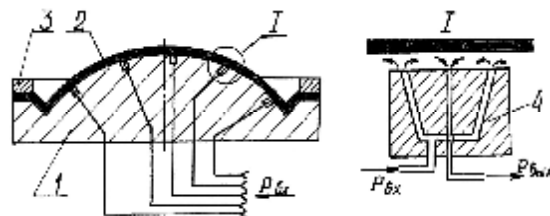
Вариант расположения струйных датчиков для определения прилегания заготовки к матрице: 1 – матрица; 2 – заготовка; 3 – прижимное кольцо; 4 – корпус датчика; $P_{\text{вх}}$ – питающее давление; $P_{\text{изх}}$ – измеряемый параметр
